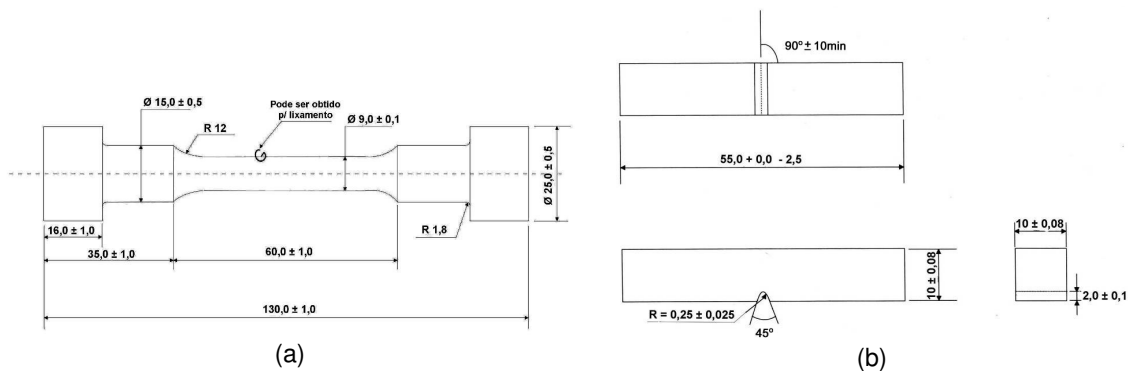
Corpo de prova utilizado no ensaio de (a) tração e (b) impacto. Dimensões em mm.
